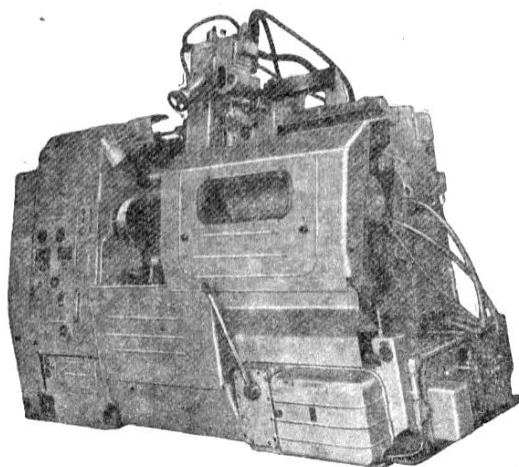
Токарно – копіювальний багаторізцевий напівавтомат модель 1722
